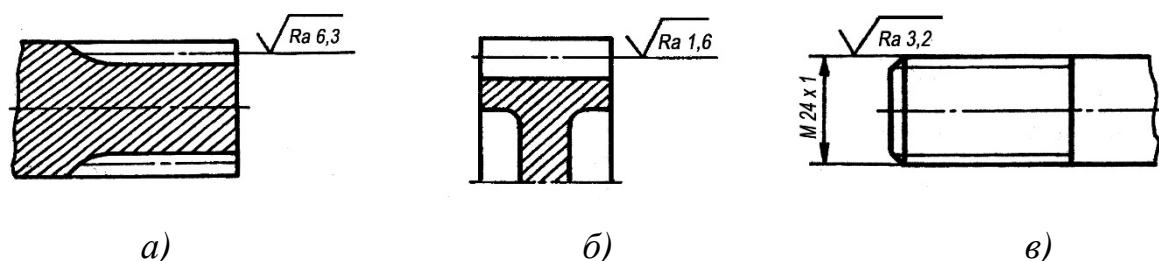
Обозначение шероховатости на шлицах, зубьях и резьбе
